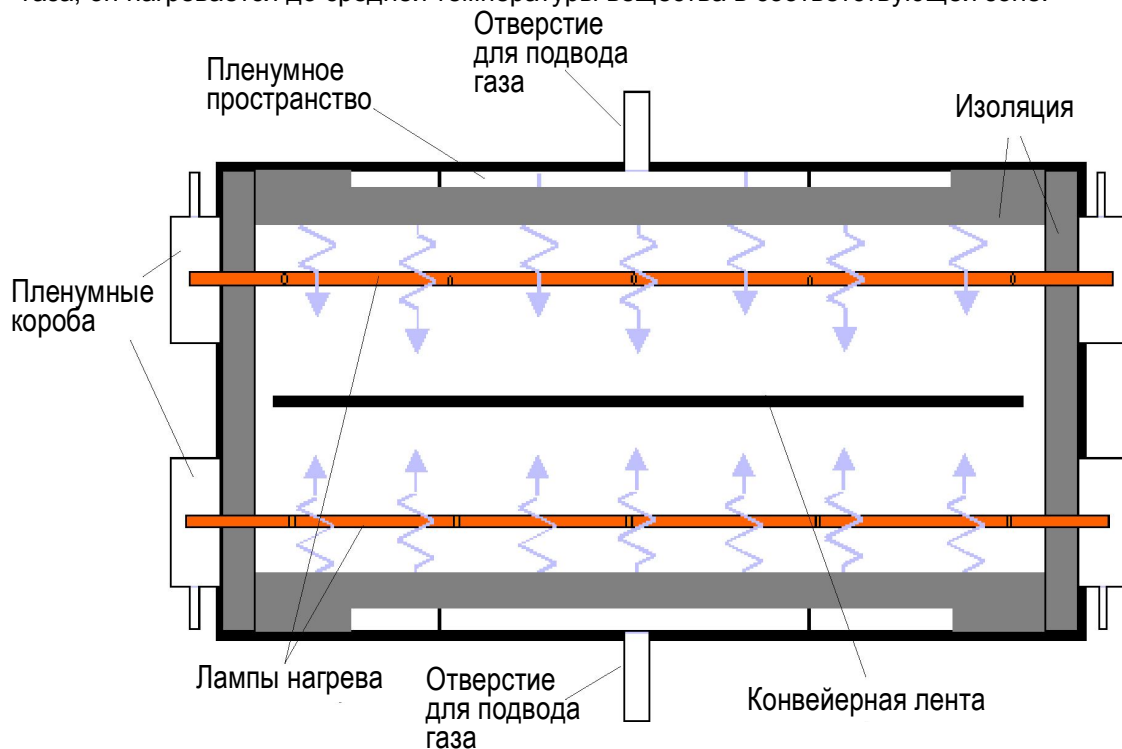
Конструкция камеры нагрева. Вид сбоку
